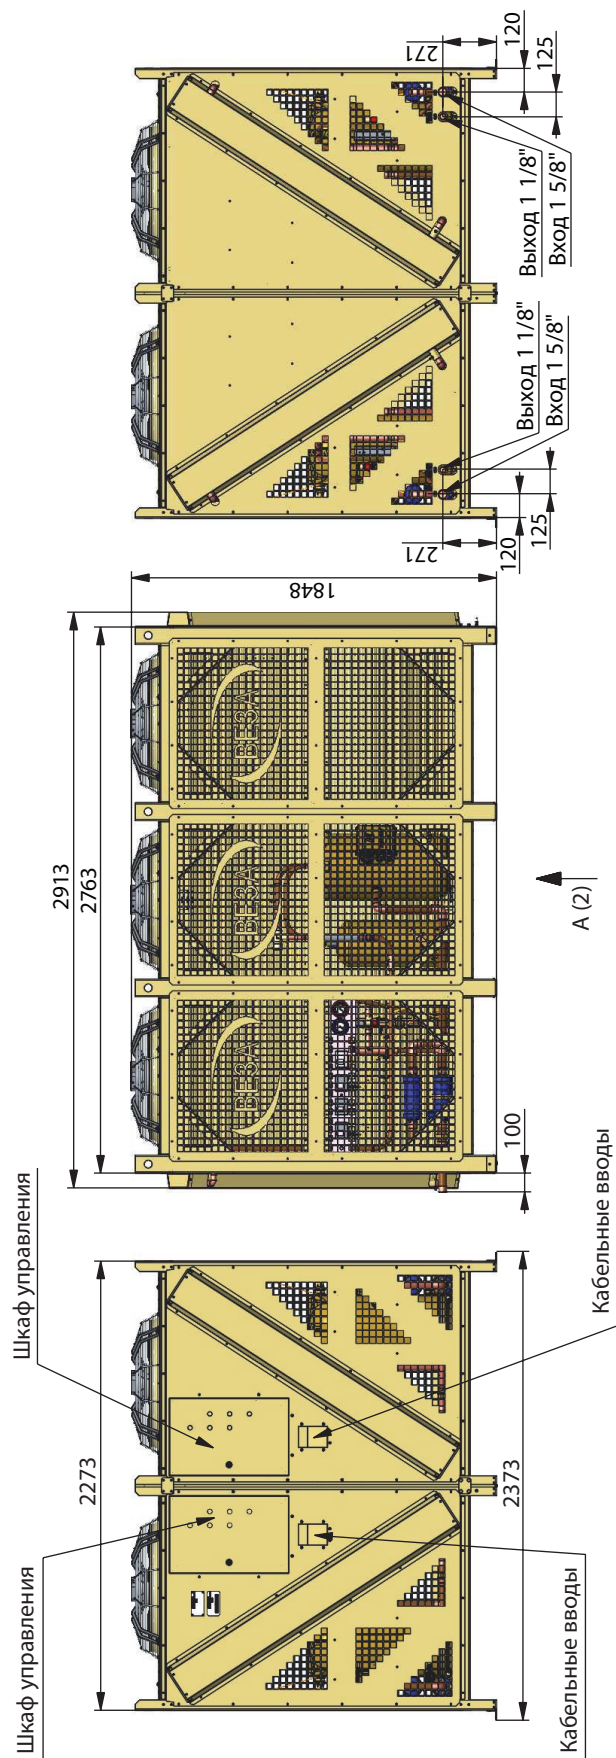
Агрегат компрессорный МАКК 120-1902
